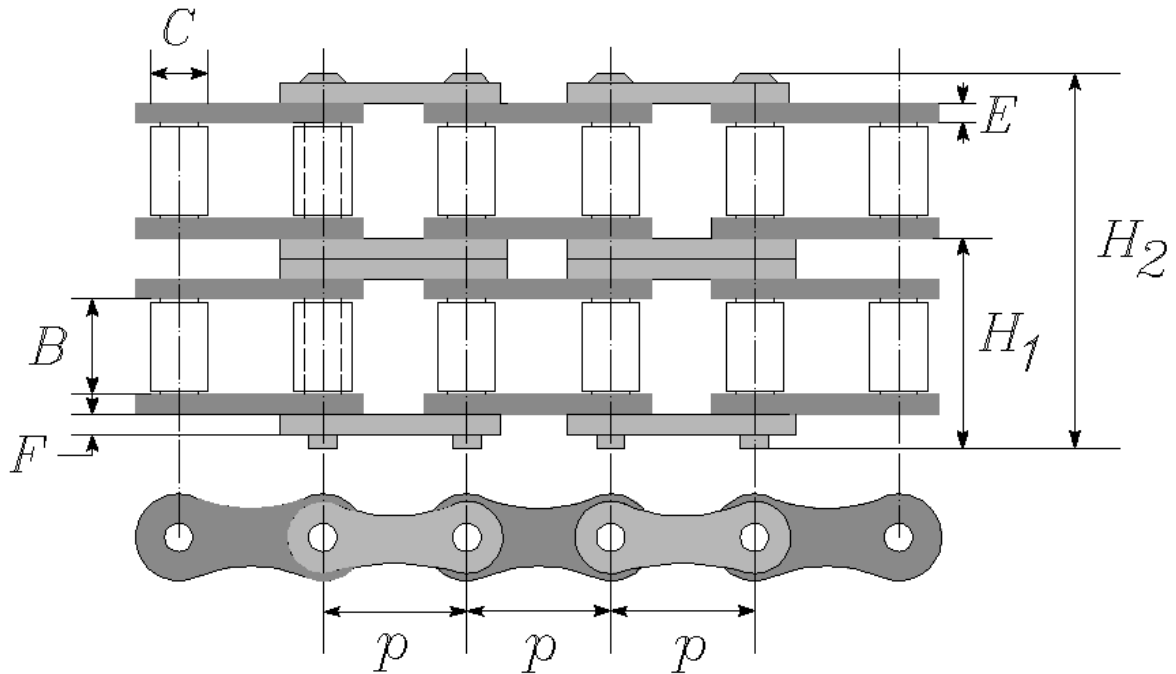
Dimensionamiento de una cadena de rodillos.
